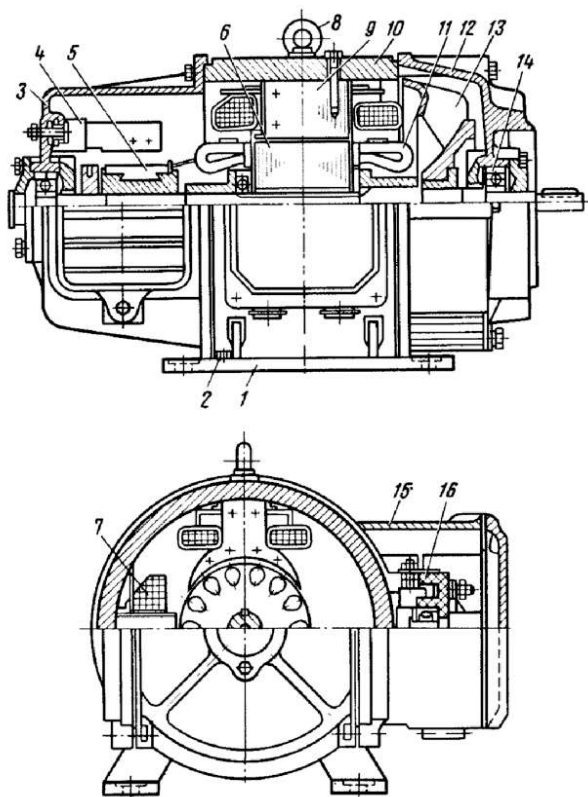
Електродвигун П-31 допоміжного компресора струмоприймача електропоїзда: 1 - лабети; 2 - гвинт заземлення; 3, 72 - підшипникові шиті; 4 - траверси; 5 - колектор; 6 - якір; 7 - додаткові полюси; 8 - рем-болт; 9 - головні полюси; 10 - станина; 11 - обмотка якоря; 13 - відцентровий вентилятор, 14 - кулькові підшипники; 15 - затискна коробка; 16 - дошка затисків.
